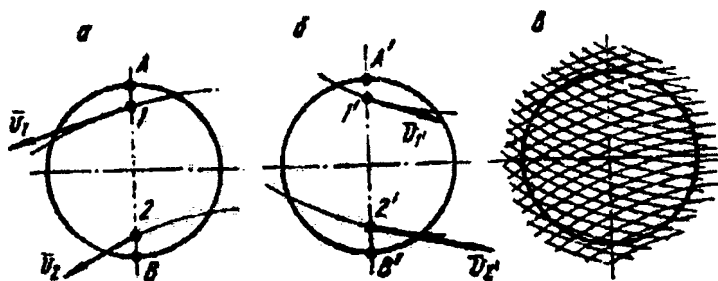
Схема нанесения следов режущего инструмента на обрабатываемую поверхность: а, б – формирование обрабатываемой поверхности на входе рабочей зоны и выходе из нее; в – сетка следов инструмента на сферической торцовой поверхности после обработки.
